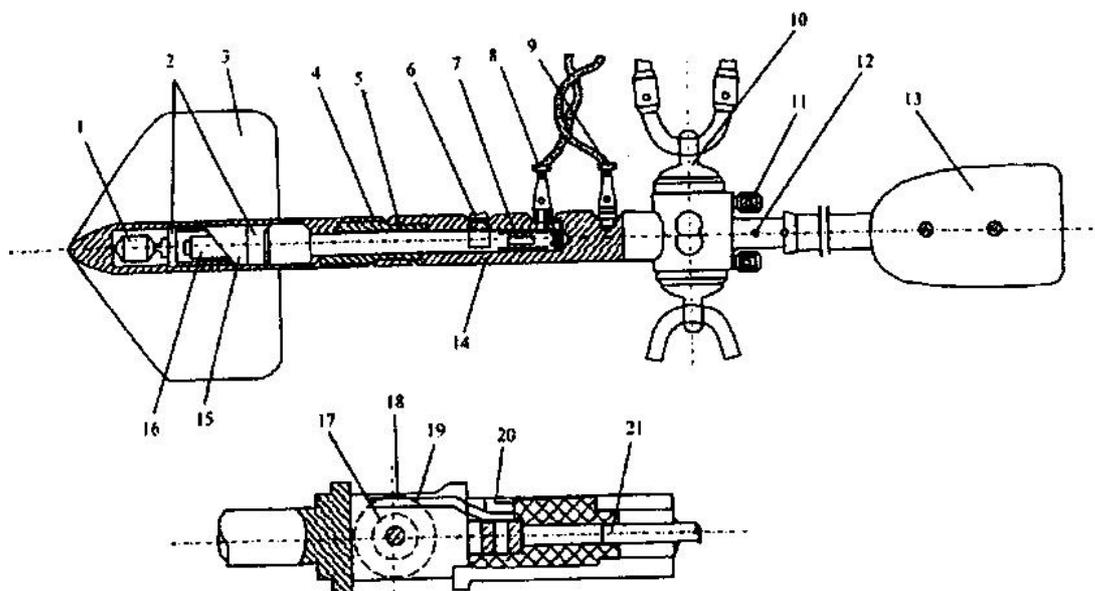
Устройство гидрометрической вертушки ГР-21М:
